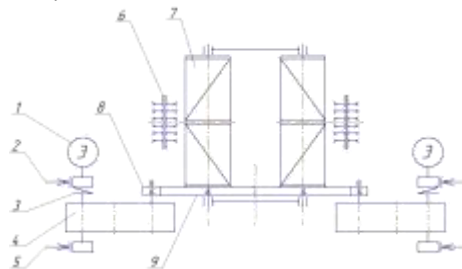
Типовая конструкция механизма подъёма (схема №1)
